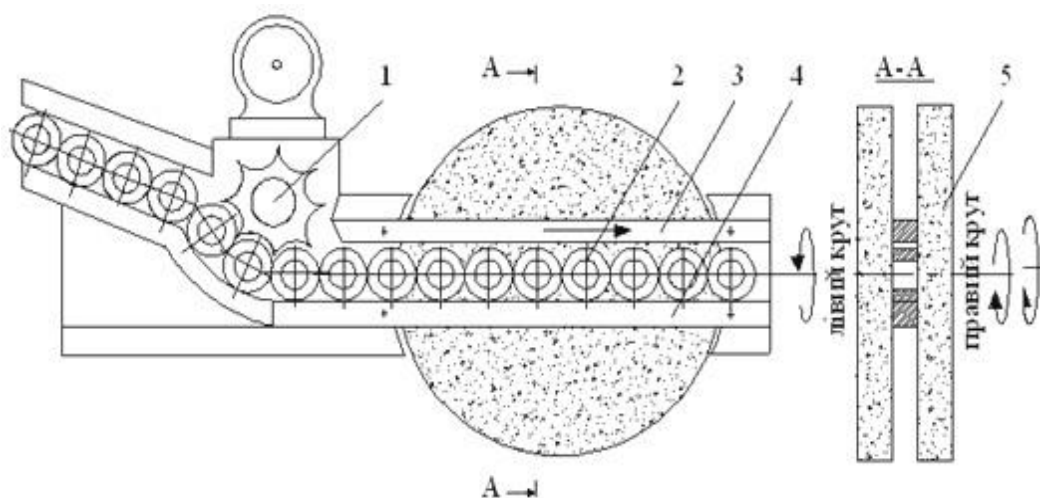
Схема абразивної обробки торців кілець підшипників [14]:
